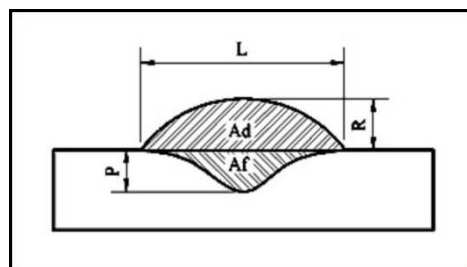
Seção transversal de um cordão de solda, onde: Ad é a área adicionada e Af é a área do metal de base fundida.
